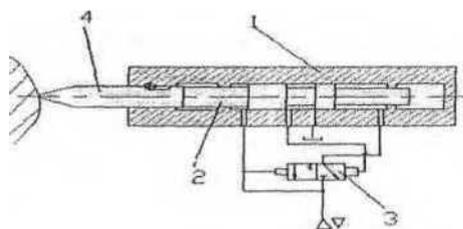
Гидрокинематическая схема ударного механизма 1 - корпус, 2 - ударник, 3 - распределитель, 4 - рабочий инструмент.
